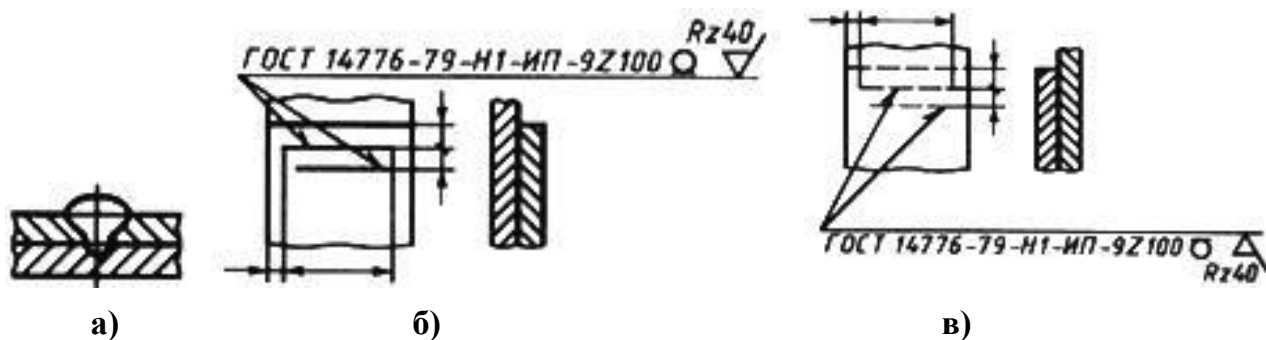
Пример обозначения сварного шва [5]: а – форма поперечного сечения шва; б – обозначение с лицевой стороны; в – обозначение с оборотной стороны
